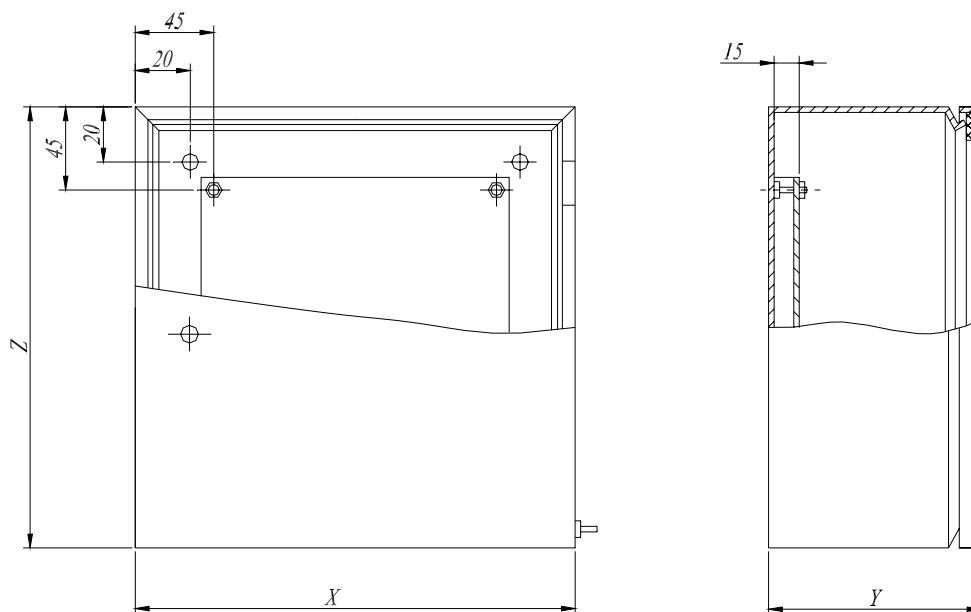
Общий вид корпусов (32X - навесной, 225 - напольный).
